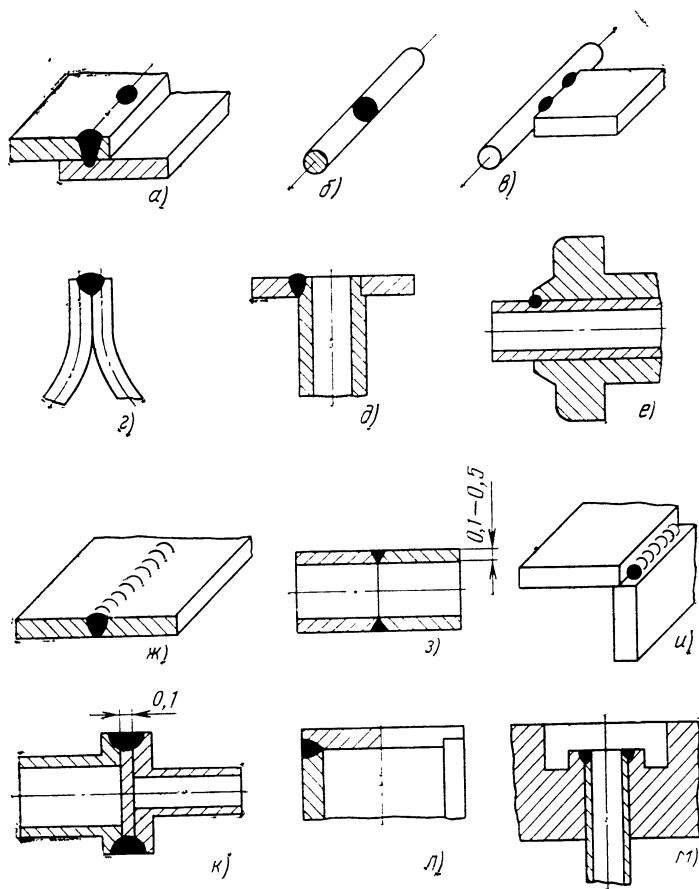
Разделка кромок и примеры конструкций для условий лазерной сварки лучом импульсных твердотельных лазеров:
